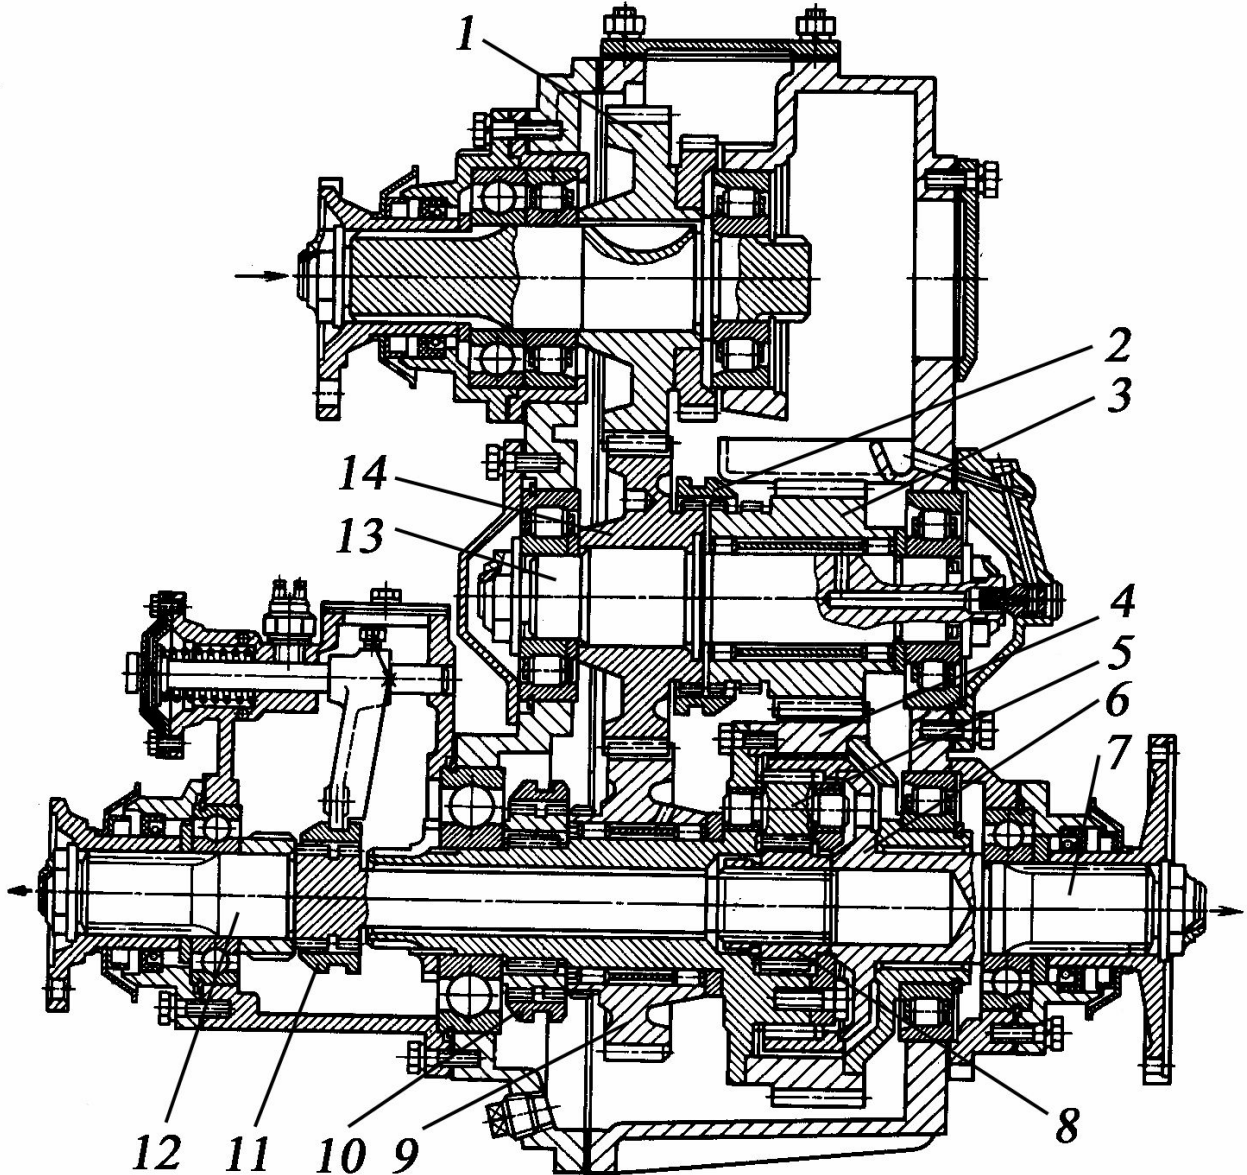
Раздаточная коробка автомобиля КамАЗ-4310
